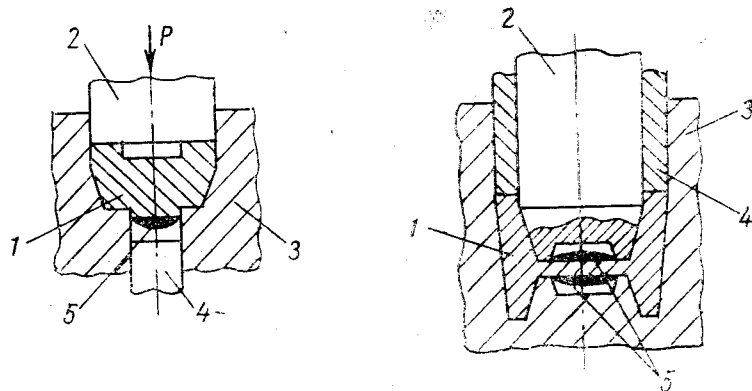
Закриті штампи з компенсаторами неточності маси заготованок:
